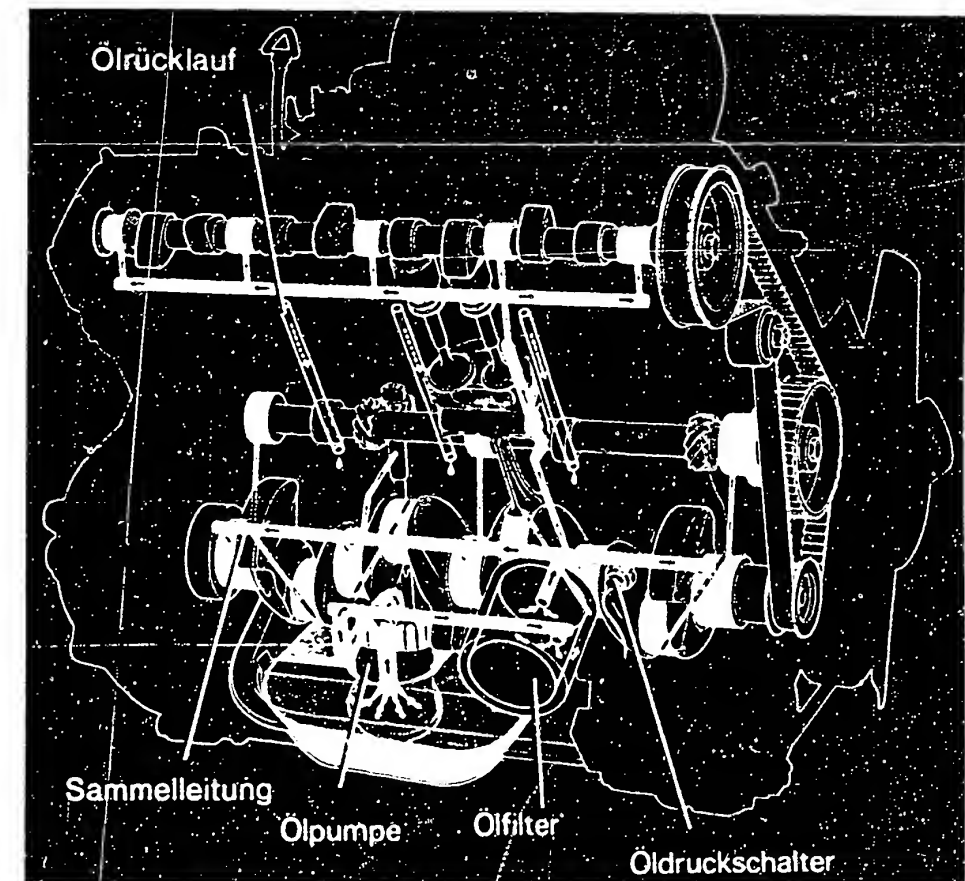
Druckumlaufschmierung mit Ölfilter im Hauptstrom.
